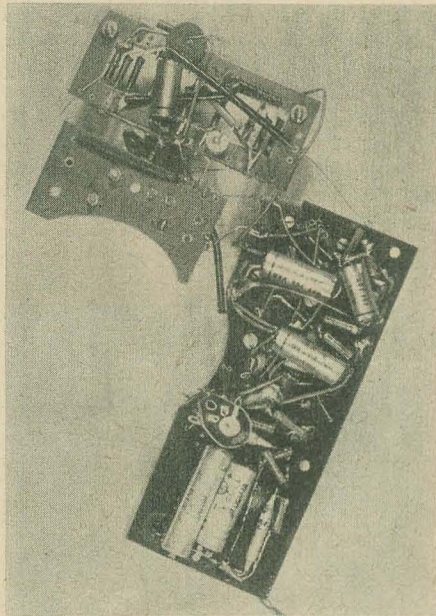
Chassisunteransicht des HF-Rahmenchassis, der Spulenträgerplatte und des ZF-Teiles
